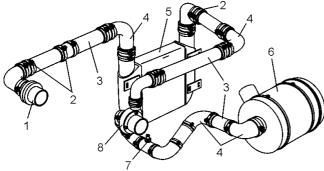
Система питания двигателя воздухом 1— труба воздухоподводящая; 2— хомуты; 3— труба; 4— патрубок; 5— охладитель наддувочного воздуха; 6— фильтр воздушный; 7— датчик сигнализатора засоренности фильтра; 8— турбокомпрессор
